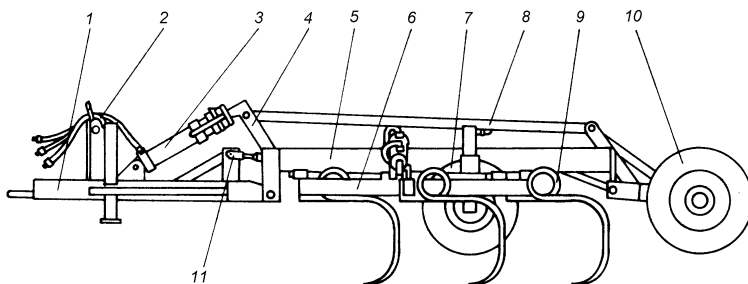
Схема культиватора КЧ-5,1: 1 – сница; 2 – гидросистема; 3 – гидроцилиндр; 4 – механизм подъема; 5 – рама; 6 – рамка; 7 – колесо опорное; 8 – тяга; 9 – рабочий орган; 10 – колесный ход; 11 – винт
